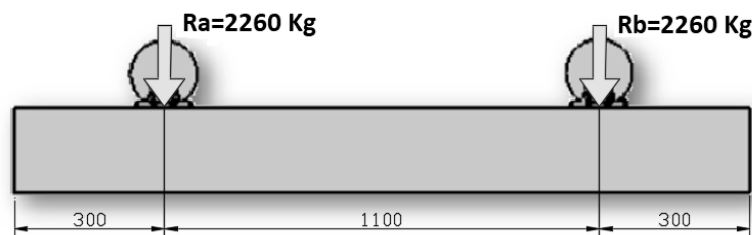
Cargas sobre el travesaño de la mesa soporte
